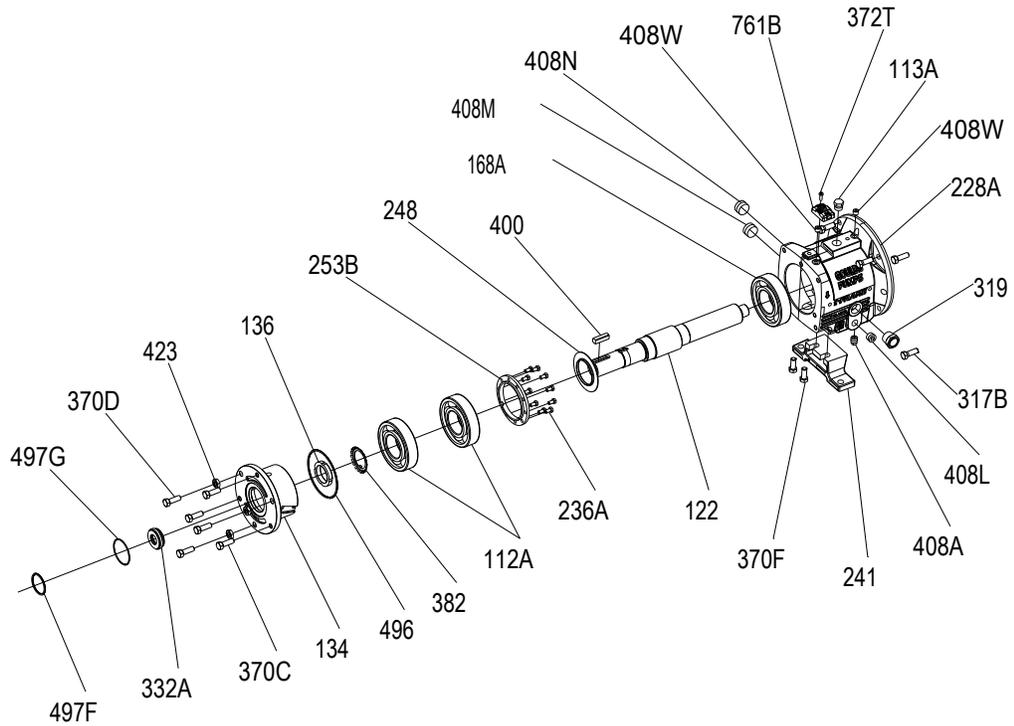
Plano de la sección transversal del modelo HT 3196
